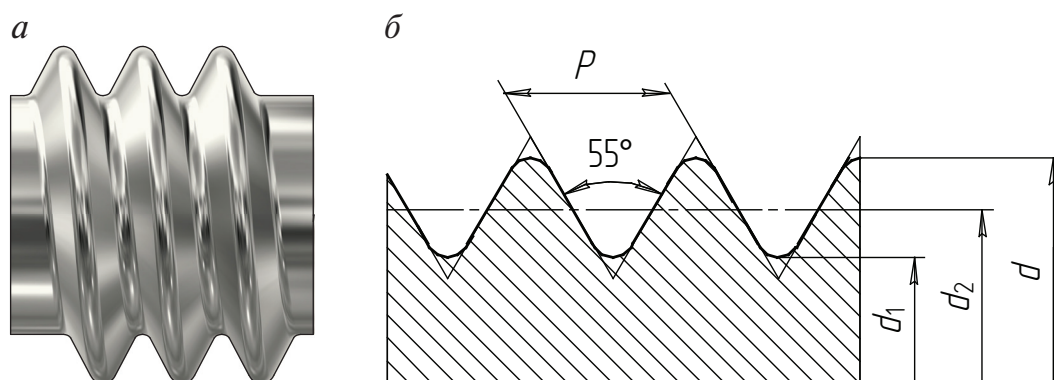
Изображение (а) и профиль (б) трубной цилиндрической резьбы
